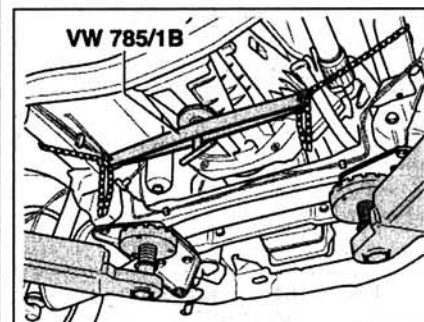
Установите под коробку передач крепежное приспособление VW785/1B.
